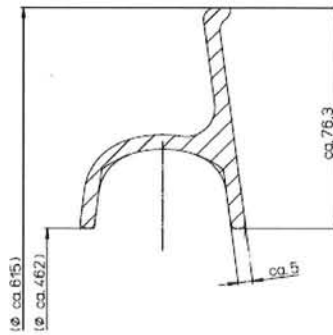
Vue en coupe joint rehausse – dalle de répartition
